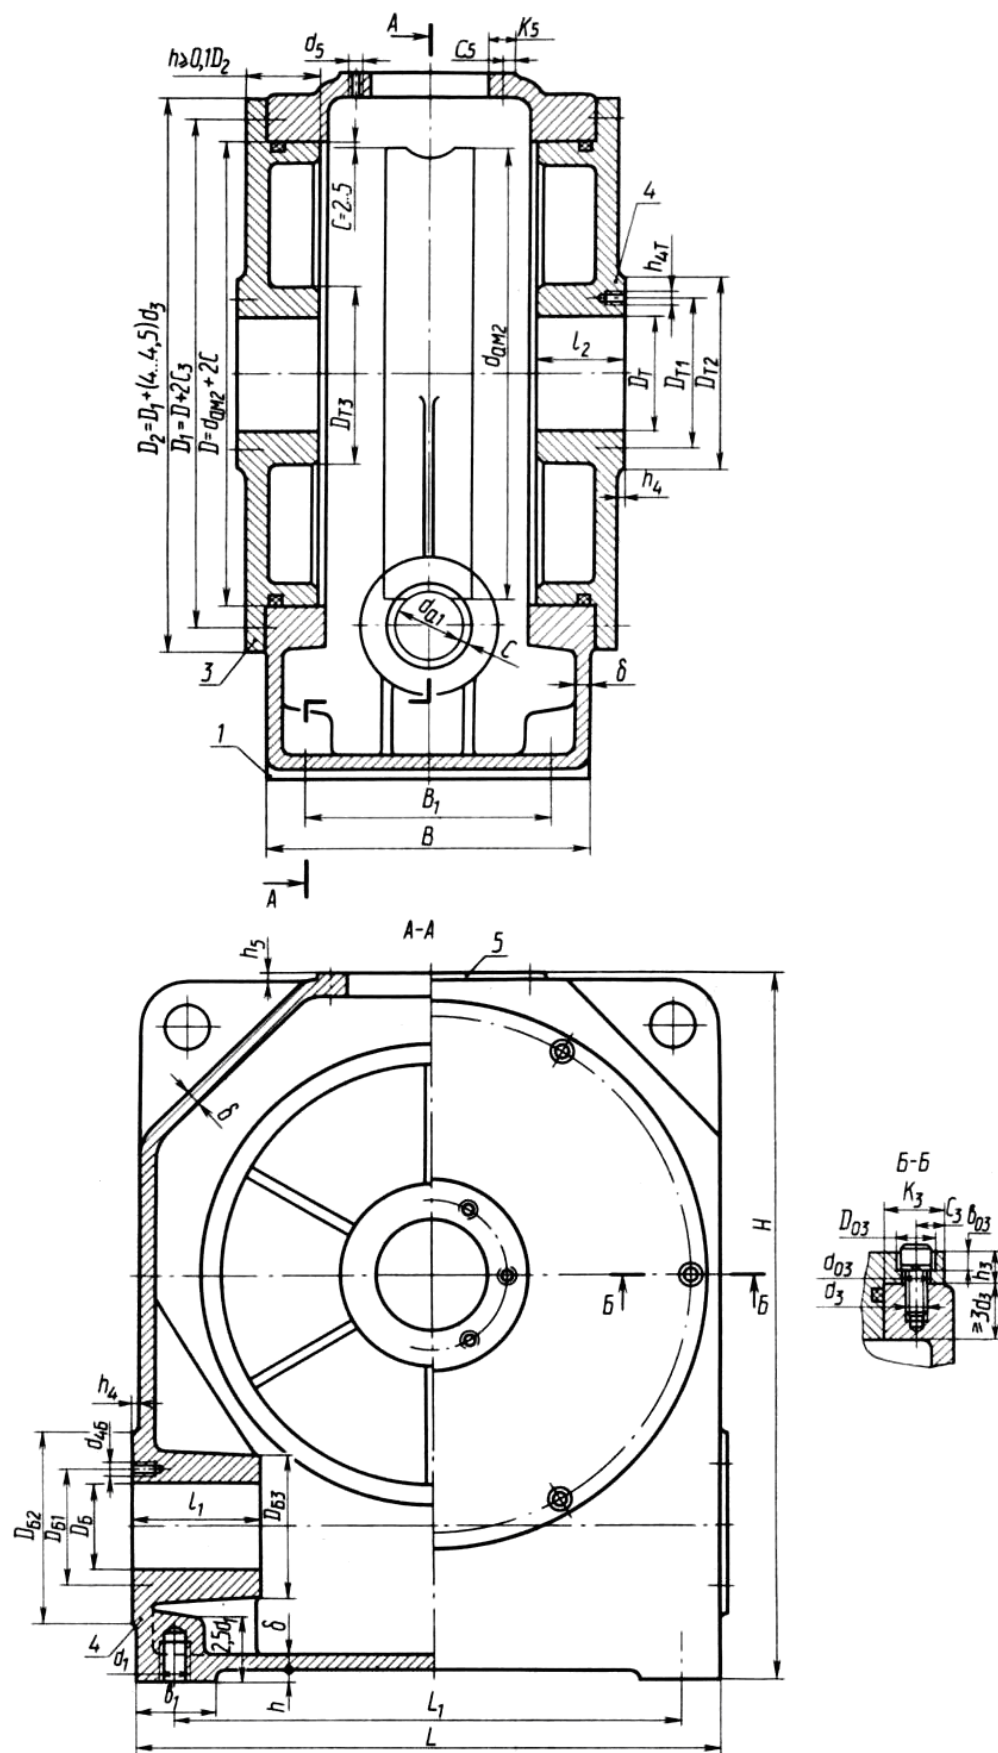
Неразборный корпус червячного редуктора с боковыми крышками
